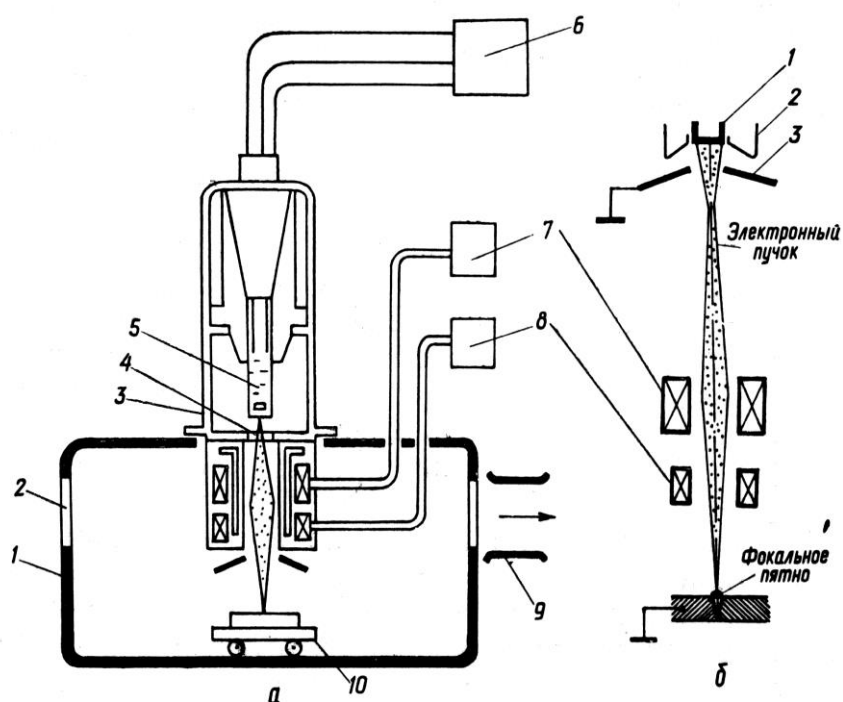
Схема электронно-лучевой сварки:
